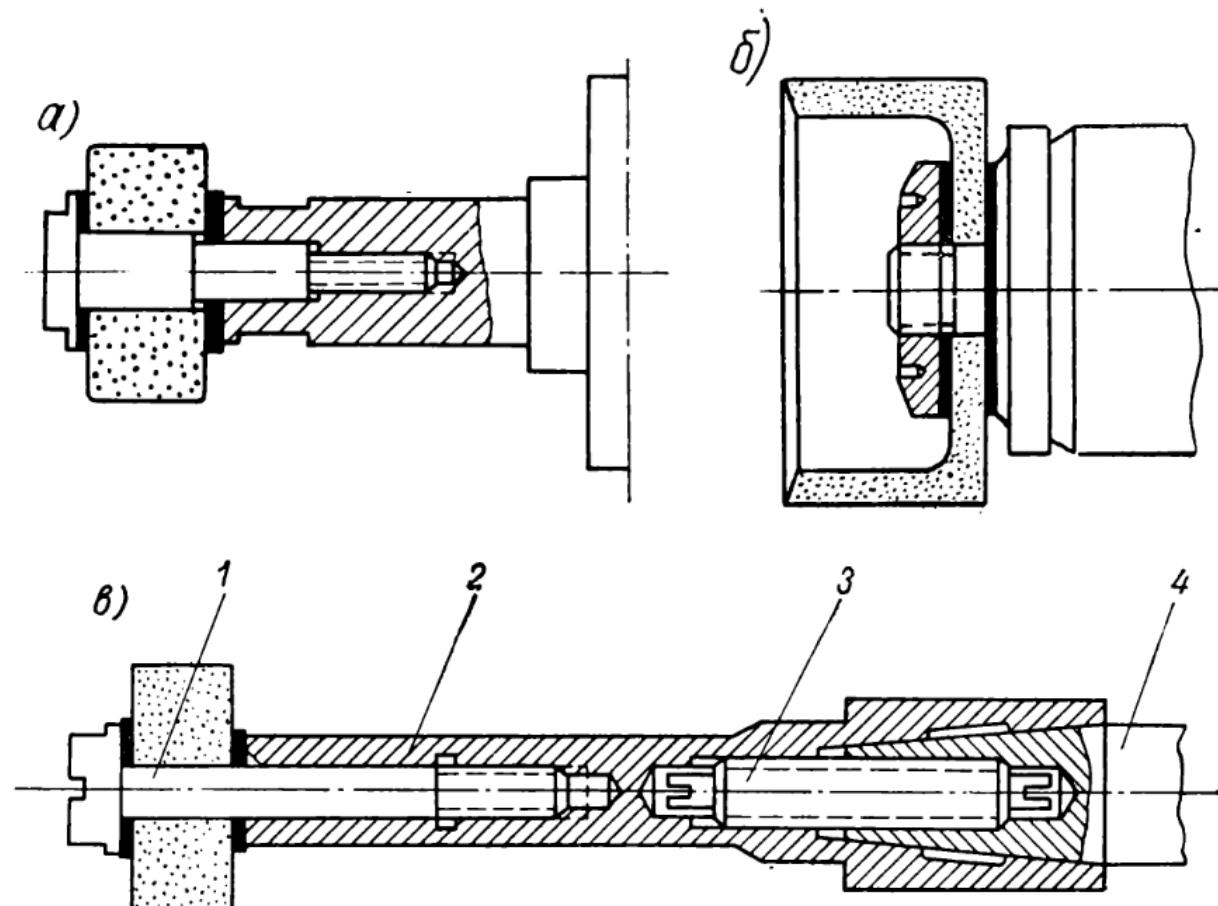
Закрепление шлифовального круга на шпинделе: *а* — через оправку для шлифования отверстия; *б* — через оправку для шлифования торца; *в* — через удлинитель
